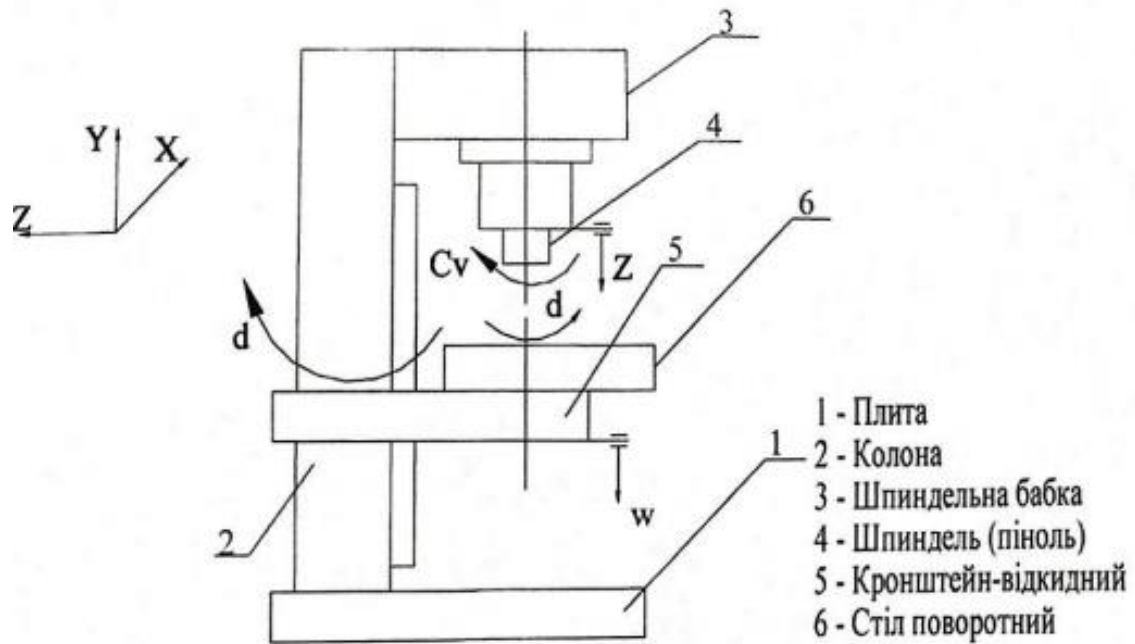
Типова компоновка вертикально-свердлильного верстату
